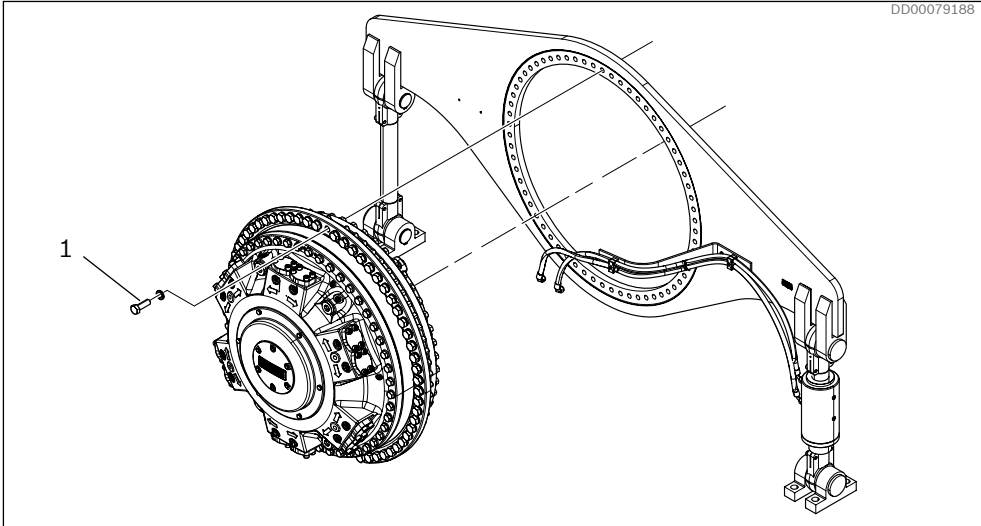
Montagem do braço de torque de duas terminações DTCBM 1600 a 4000 em CBm 2000 a CBm 4000
